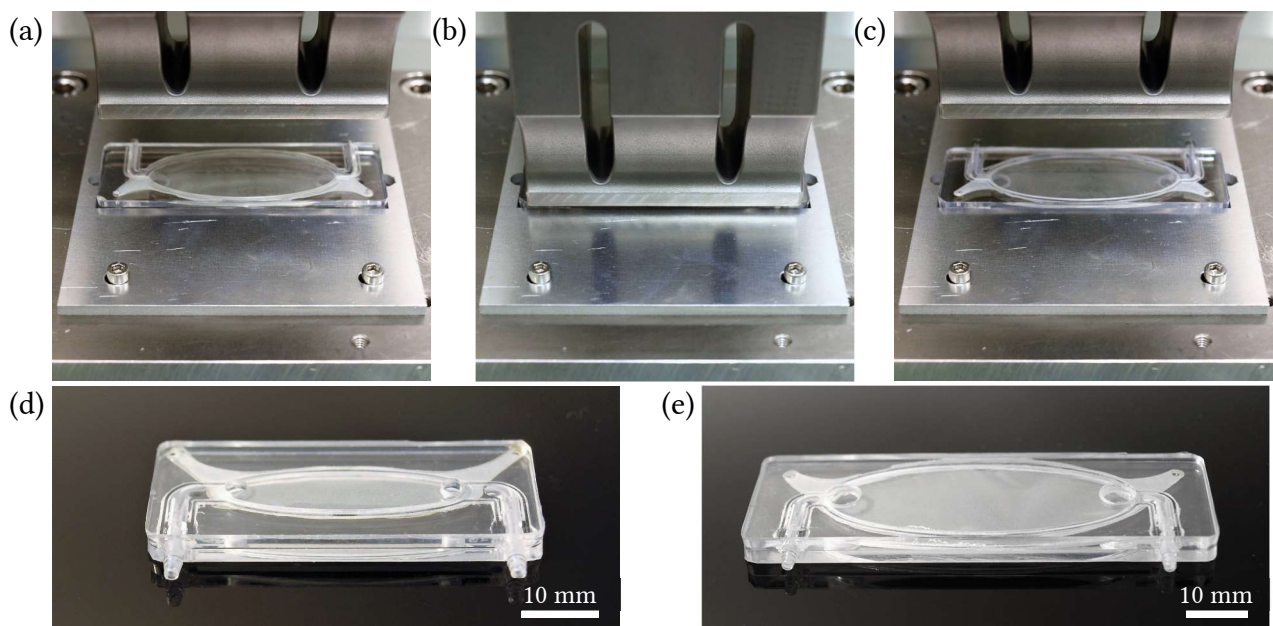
Schritte zum Ultraschallschweißen der Chiphälften und der Schlauchanschlüsse. (a) Einlegen aller Komponenten, hier am Beispiel des 800 μl -MBR, (b) Ultraschallschweißen, (c) verschweißter 800 μl -MBR, (d) ultraschallgeschweißter 100 μl -MBR, (e) ultraschallgeschweißter 800 μl -MBR.
